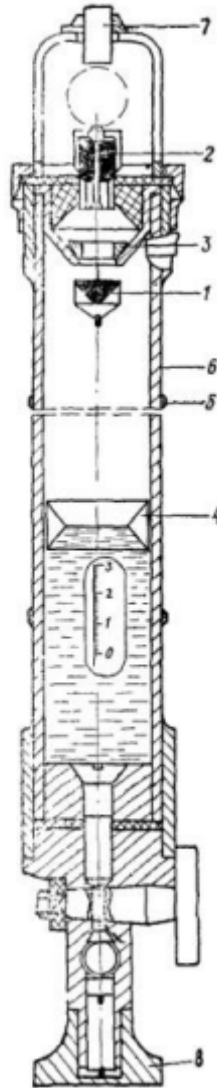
Переносний гідростатичний нівелір НШТ-1: 1 – клапан-поплавець; 2 – циліндр автоматичного клапана; 3 – скляний циліндр автоматичного клапана; 4 – кільцевий порожнистий поплавець; 5 – металевий корпус; 6 – скляний циліндр водомірної склянки; 7 – верхня п'ята, укріплена в корпусі на різьбленні; 8 – нижня п'ята
